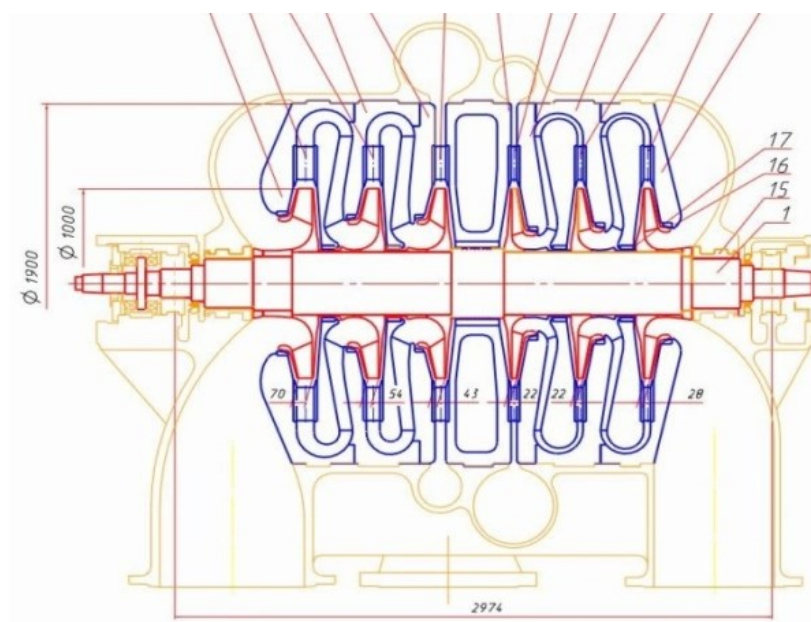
Продольный разрез ЦВД модернизированного компрессора
